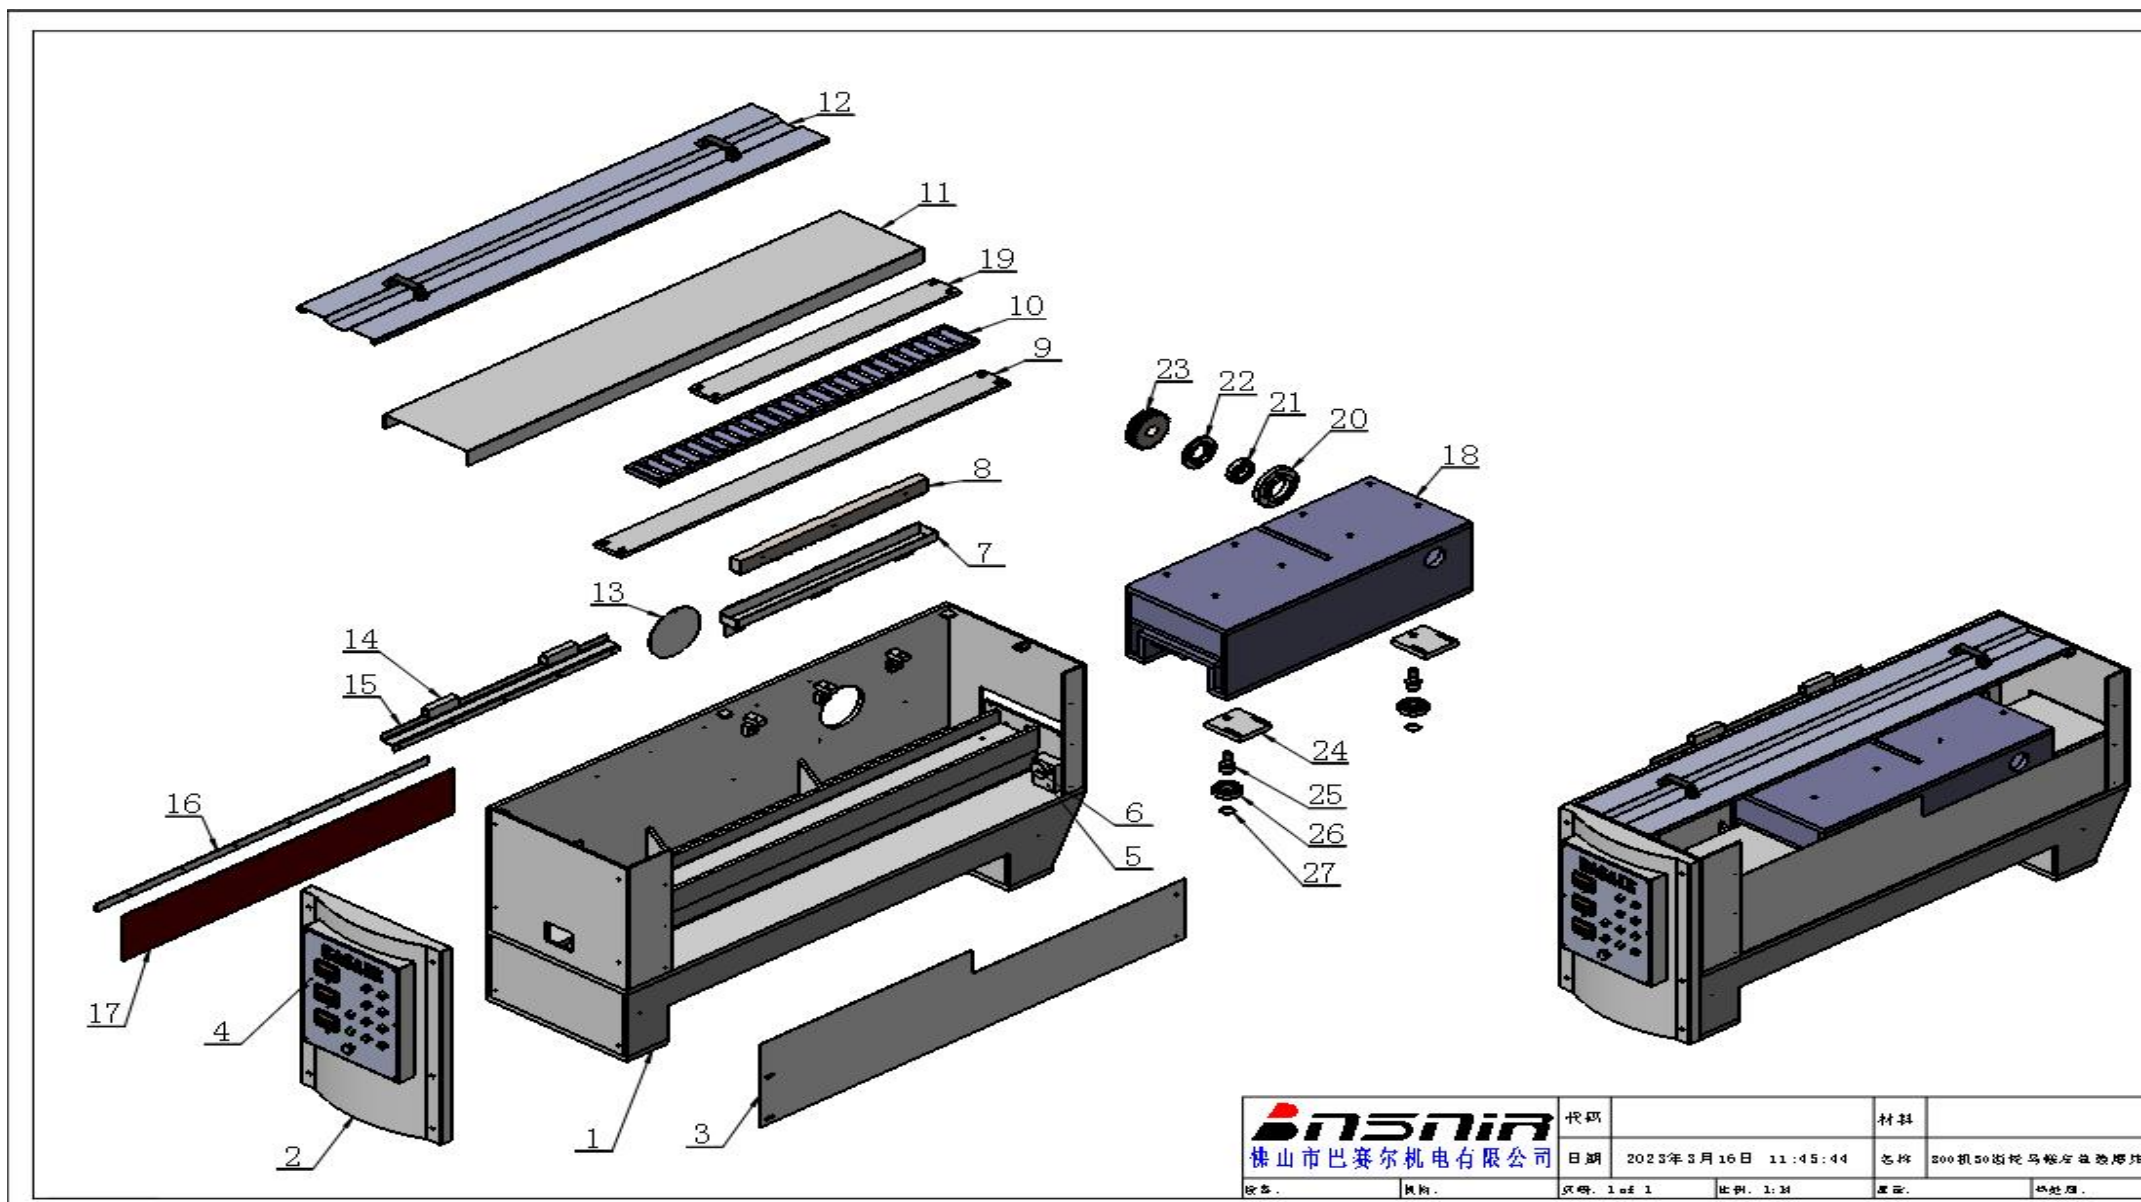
1 BP1000/16 抛光机——马鞍(左)装配图 picture3-1 Assembly drawing of BP1000/16 polishing machine -- saddle (left)
